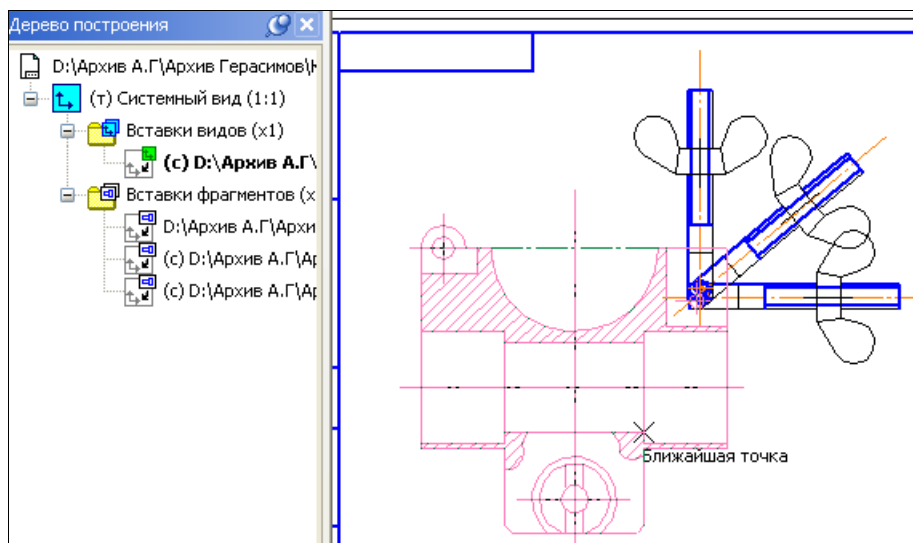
Чертеж Корпус с винтами и Деревом построения
